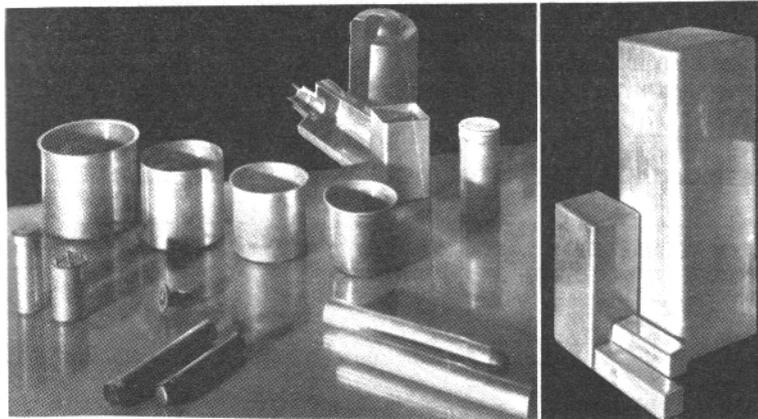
Piezas fabricadas por extrusión en frío.
